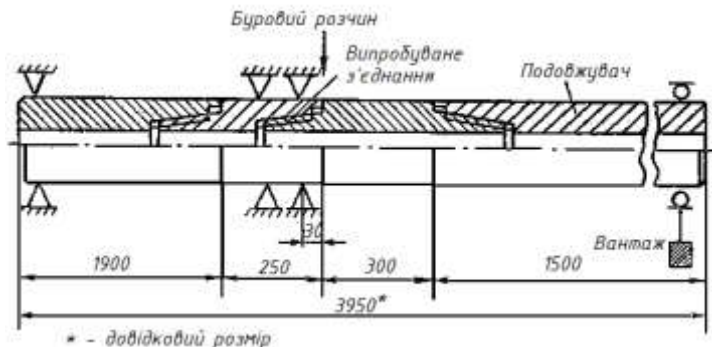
Конструкція зразка для випробувань замкових різьб 3-121 на корозійну втомленість
